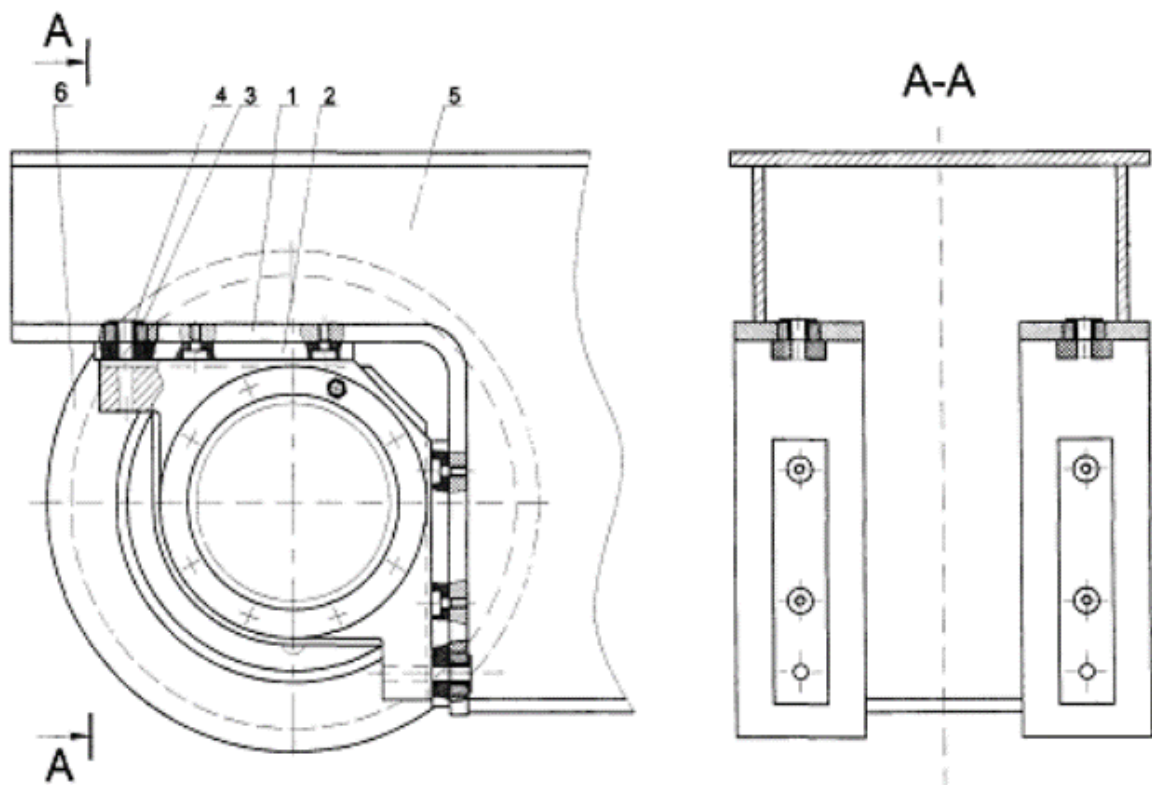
Буксовий вузол – загальний вигляд: 1 – гнучий окантувальний елемент; 2 – поліуретанова амортизаційна прокладка; 3 – металева втулка; 4 – поліуретанова амортизаційна втулка; 5 – ділянка торцевої балки вантажного візка; 6 – ходове колесо.
